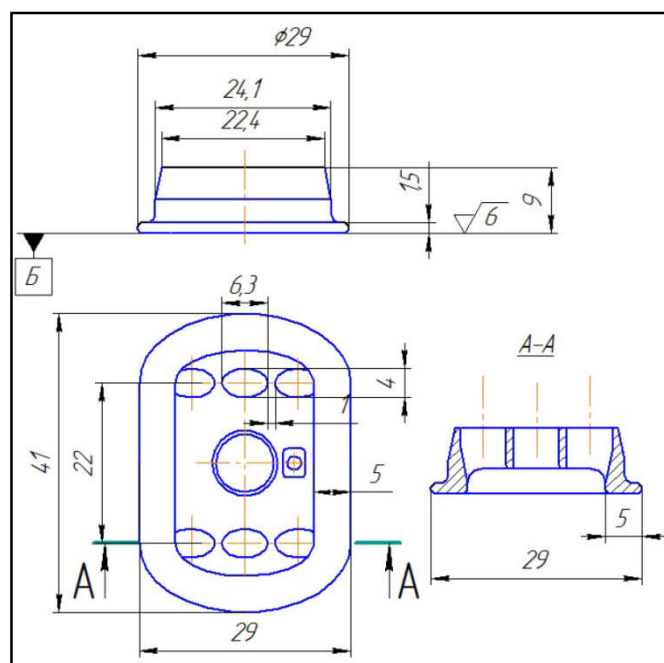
Конструктивная схема фланца для крепления овальных (эвольвентных) трубок ВВТ
